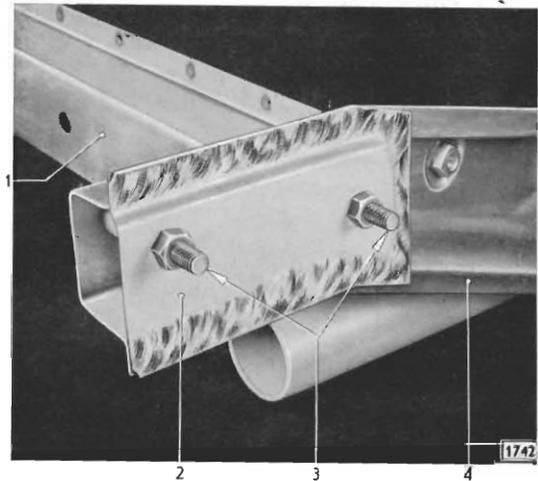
Linkes Schließblech mit zwei Sechskantschrauben und Muttern für Stoßstangenbefestigung ausgerichtet und festgeschraubt – rechtes Schließblech in gleicher Weise ausrichten und festschrauben
